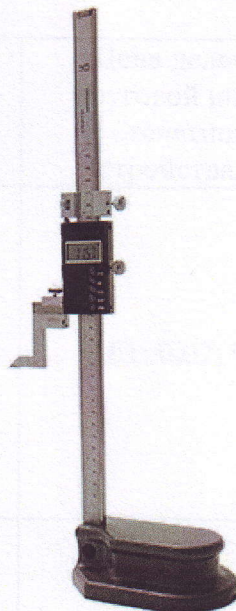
Общий вид штангенрейсмаса ШРЦ
